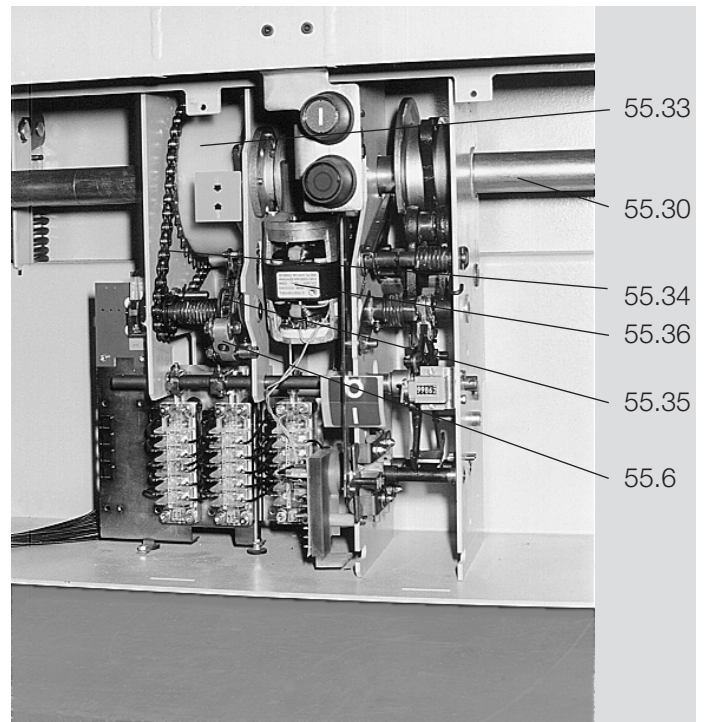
/2: Disjuntor a vácuo VD4 fixo, comando por molas pré-carregadas, placa frontal removida
